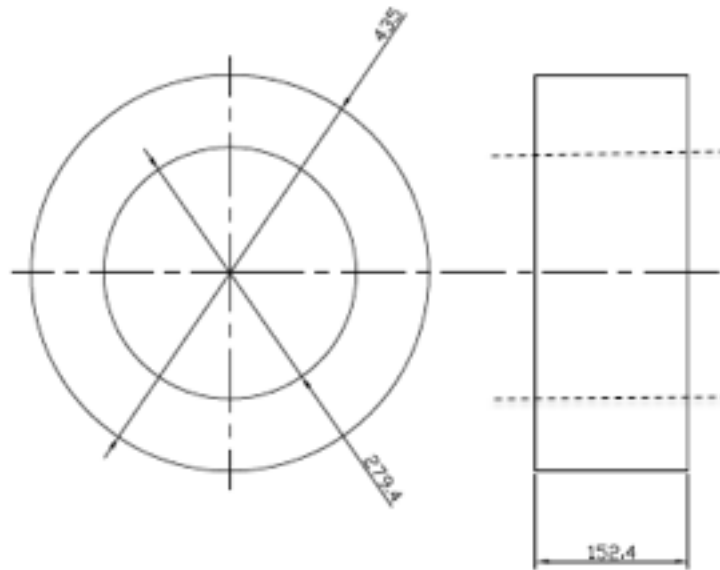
Representação das dimensões da peça a ser revestida (cotas em mm).
